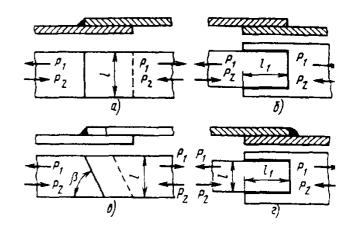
Швы нахлесточных соединений: a - лобовой; δ - фланговый; ϵ - косой: ϵ - комбинированный
